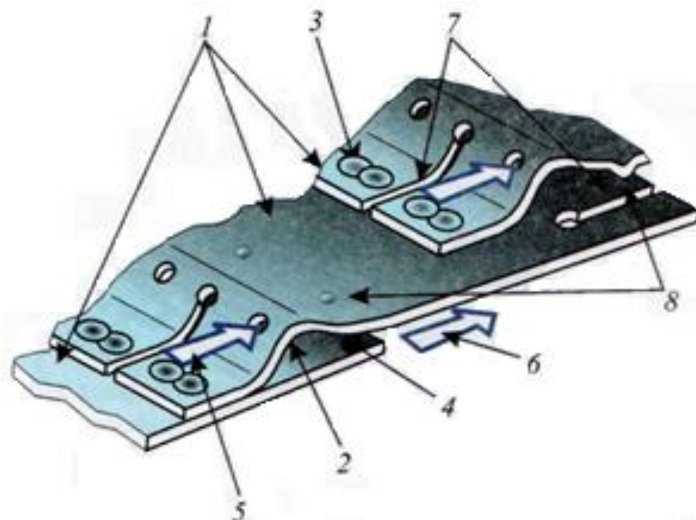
Пленочная система охлаждения из сварных секций: 1 – секция; 2 – кольцевые ребра; 3 – контактная сварка; 4 – кольцевая щель; 5 – охлаждающий воздух; 6 – заградительная пленка; 7 – компенсирующие прорезы; 8 – упор
